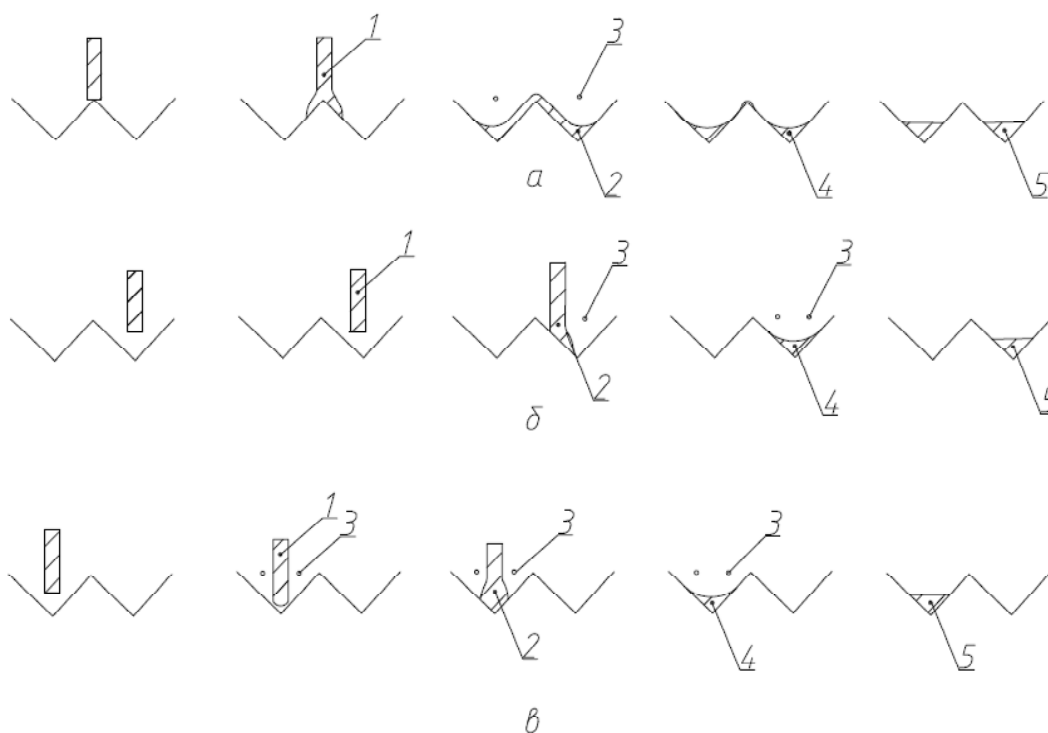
Схема соударения металлической струи с шероховатой поверхностью:
